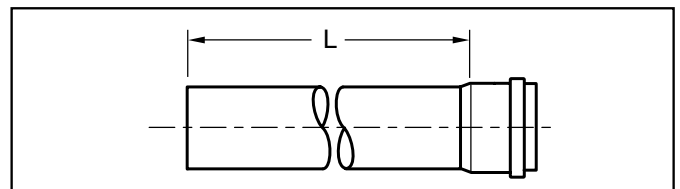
Tubo gas combusti → 110 (misure → tabella 77)
